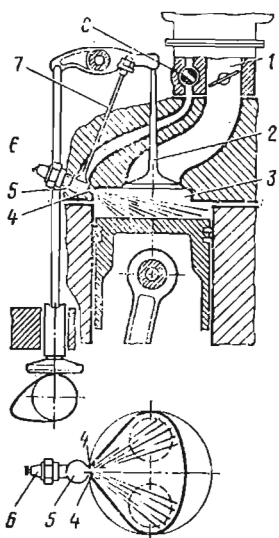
Двигатель с форкамерно-факельным зажиганием:
